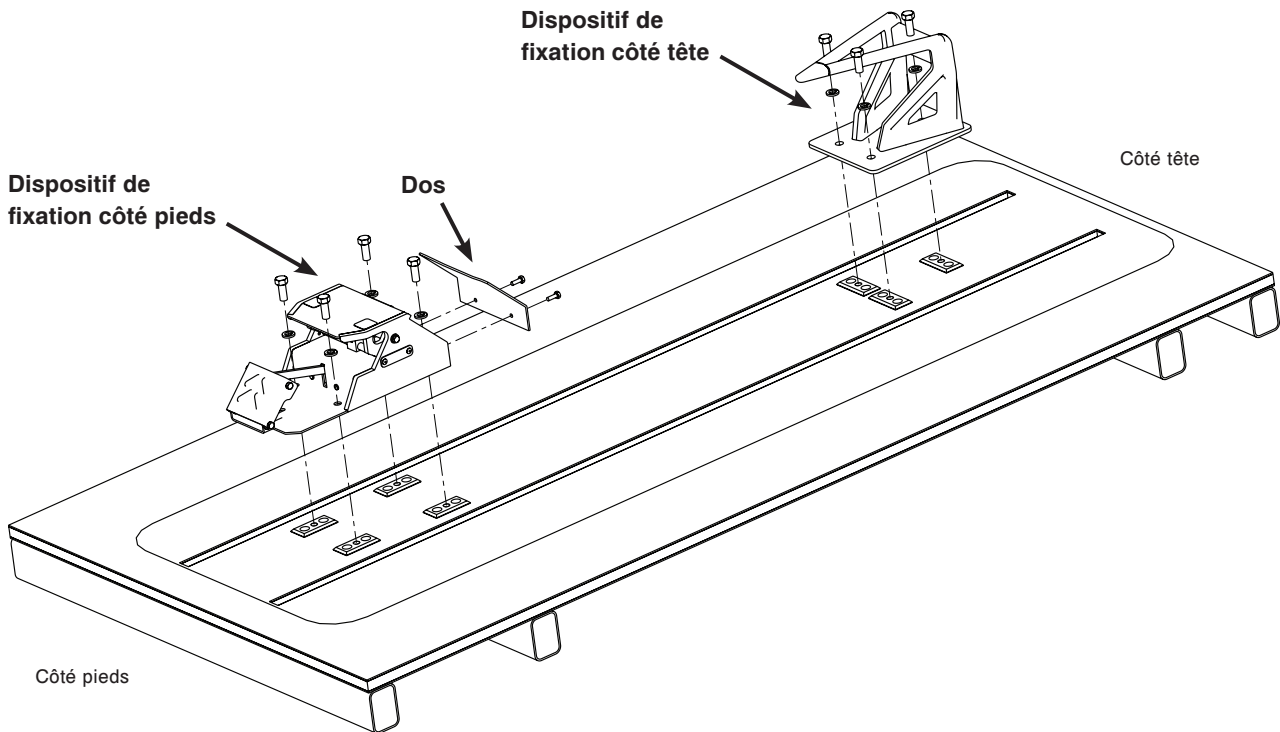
Dispositif de fixation côté tête et côté pieds – installation de la plaque de plancher
